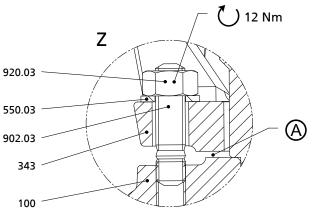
Моменты затяжки mini-Compacta US100, UZS150
